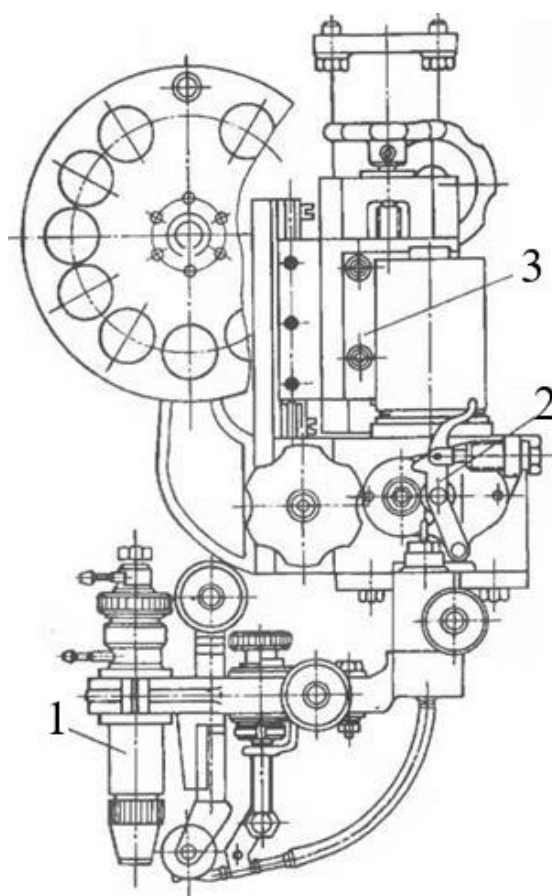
Сварочный автомат АДГ-630
